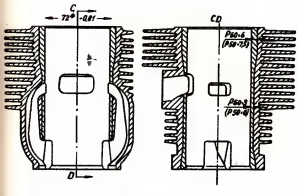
Цилиндр двигателя P-60 для автомобиля «Трабант».
